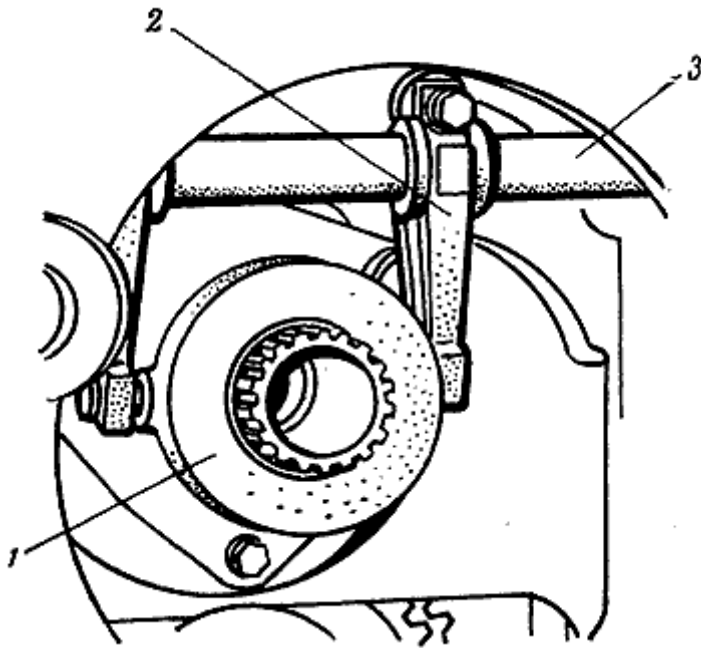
Снятие упорного подшипника, отводки, вилок включения и вала вилок сцепления:
